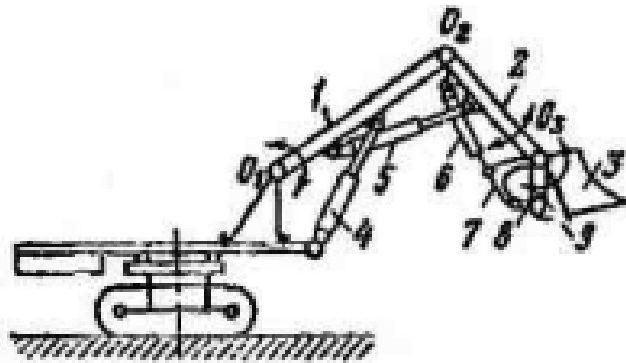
Конструктивна схема гідравлічного екскаватора пряма лопата напірна з поворотним щелепним ковшем
